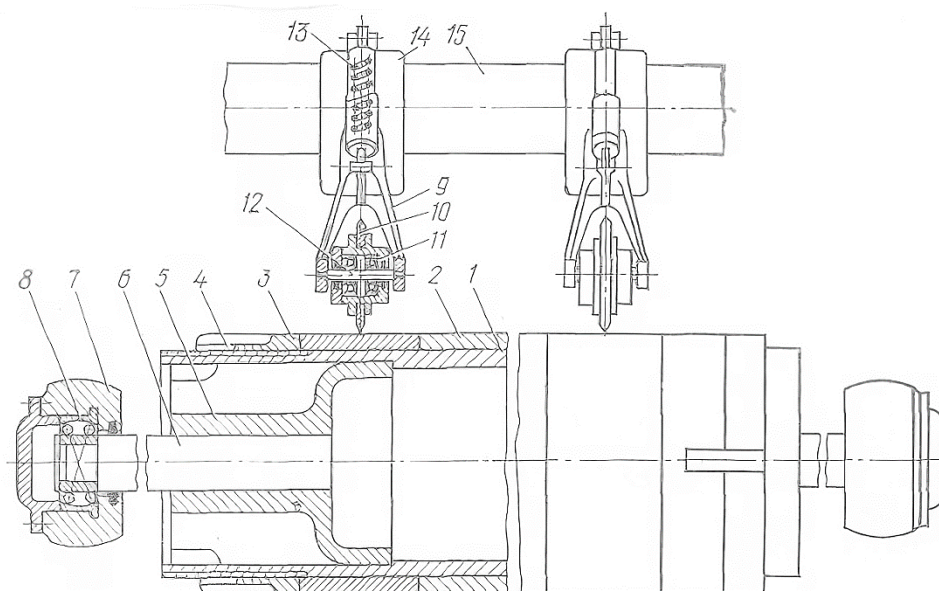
Конструкция ножевого вала, работающего по принципу ножевого резания: 1 – труба ножевого вала; 2 – ножевой вал; 3 – гайка ножевого вала; 4 – контргайка ножевого вала; 5 – патрон; 6 – цапфа; 7 – корпус подшипника; 8 – подшипник; 9 – рычаг верхнего ножа; 10 – верхний дисковый нож; 11 – подшипник верхнего ножа; 12 – ось верхнего ножа; 13 – пружина для прижима ножа; 14 – кронштейн верхних ножей; 15 – труба для установки кронштейна
